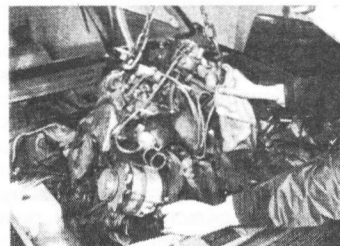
Поднятие конструкции двигателя/трансмиссии
